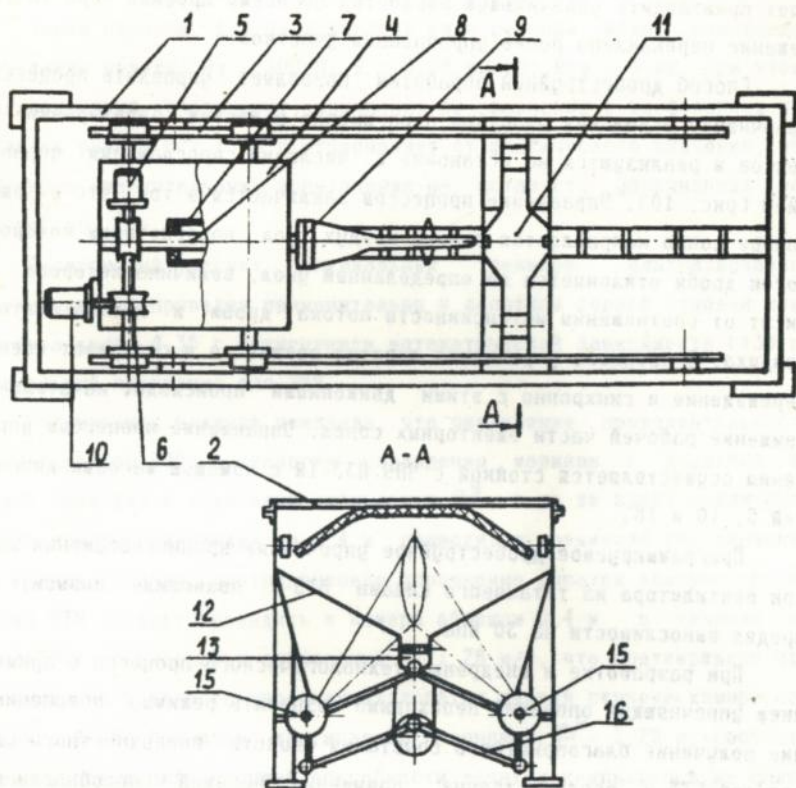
Схема установки для программируемого упрочнения крупногабаритных лопаток вентилятора ГТД: I - корпус; 2 - крышка; 3 - направляющие; 4 - каретка; 5 - электродвигатель; 6 - червячная пара; 7 - втулка; 8 - шпindel; 9 - замок; 10, 16 - шаговые электродвигатели; 11 - дробесборник; 12 - стенка; 13 - поддон; 14 - штorka; 15 - сопло.
